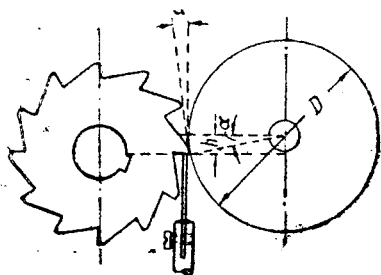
Заточка (шлифовка) задней грани зубцов развертки дисковыми кругами.
